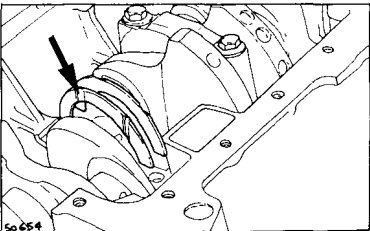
Расположение упорных полуколец коленчатого вала
